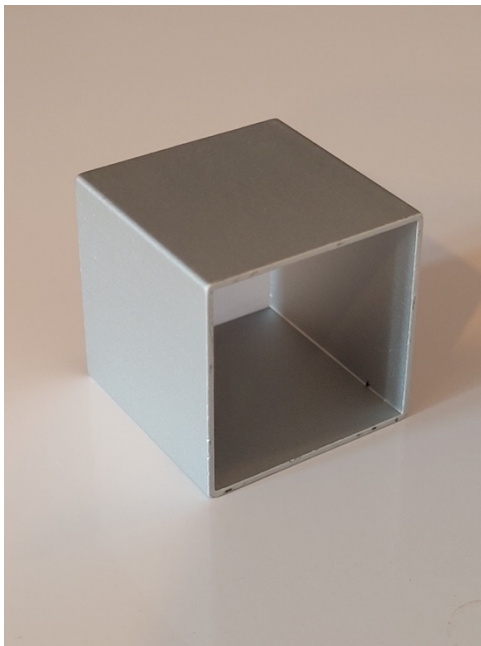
Moule de conception des échantillons vu de côté [photographie personnelle]
